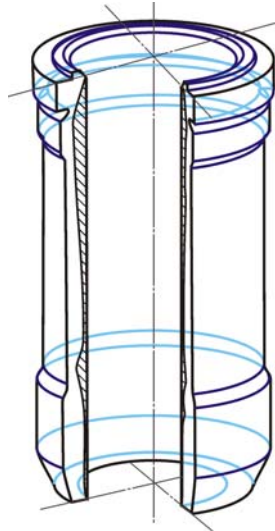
Эпюра износа рабочей поверхности гильзы цилиндра
